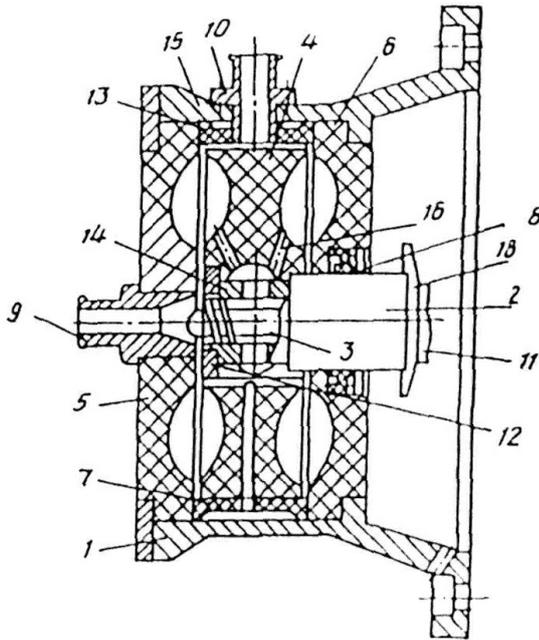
Гидродинамический нагреватель установки ПМР-02:
